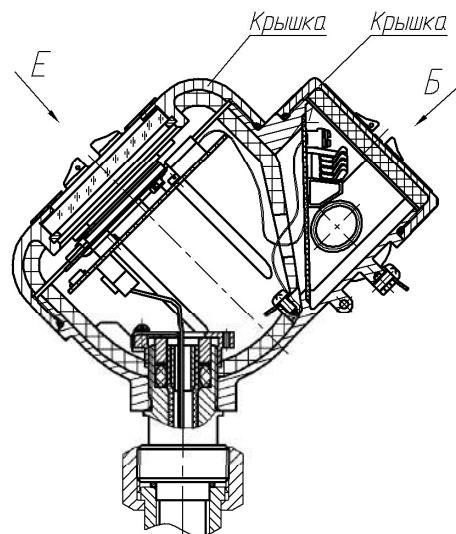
Габаритные размеры приборов (лист 3)
